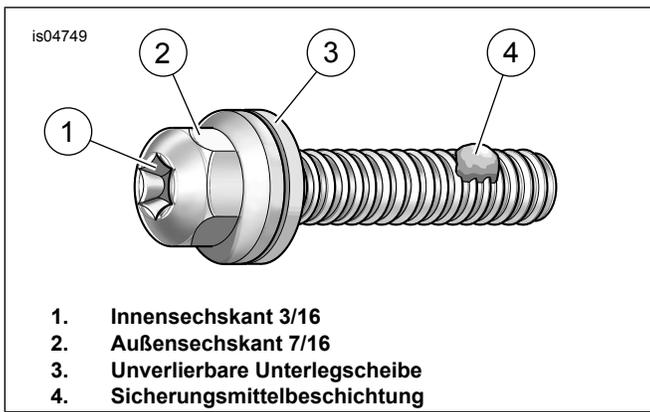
Kipphebeldeckel- oder Kipphebelgehäuse-schraube
